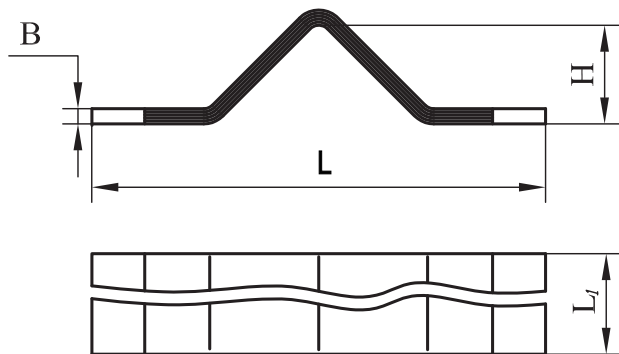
Компенсаторы шинные серии КША и КШМ со сварочным соединением
